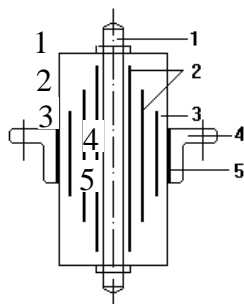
Конденсаторный бумажно-бакелитовый ввод для внутренней установки: 1 – токоведущий стержень; 2 - конденсаторные обкладки; 3 – бакелизированная бумага; 4 - металлический фланец;
